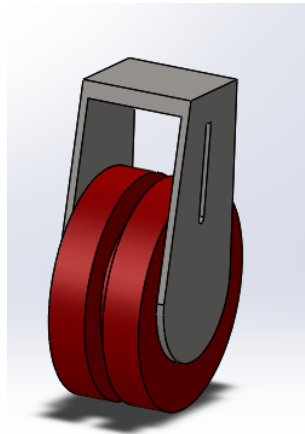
Carrete de almacenamiento del alambre Diseño 3D en SolidWorks
